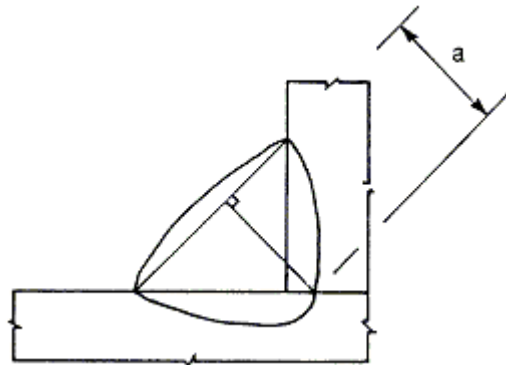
Товщина кутового зварного шва з повним проваром
